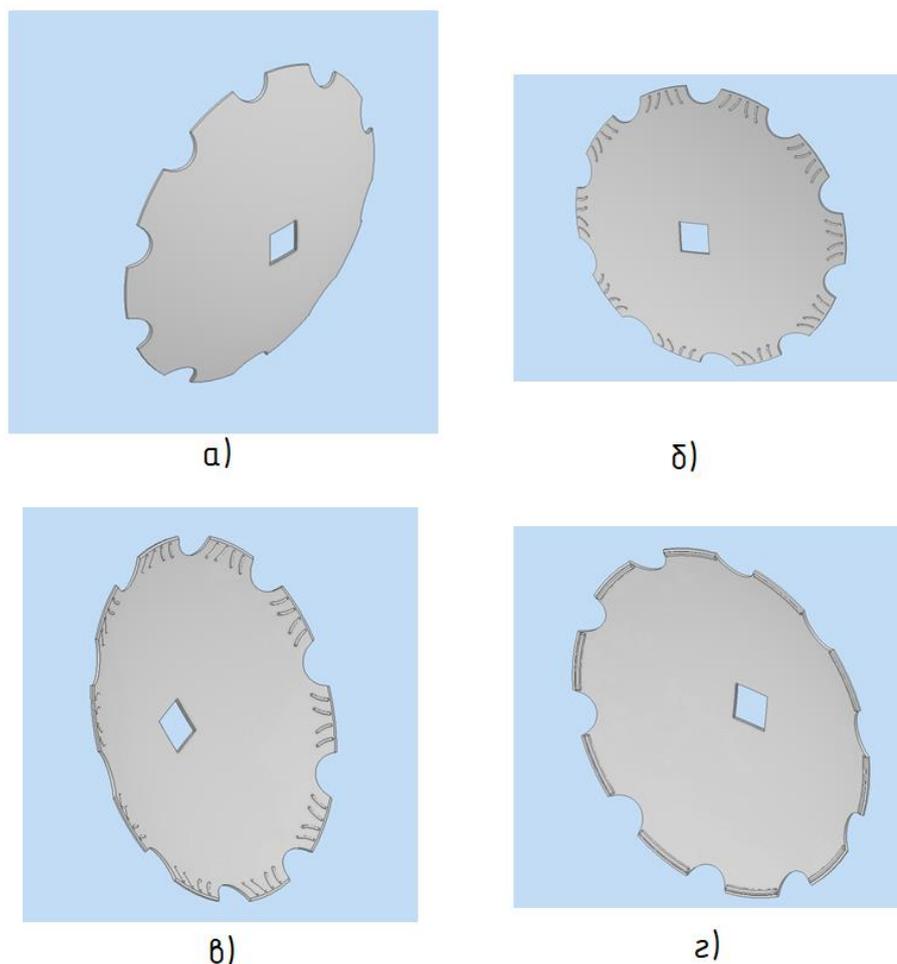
Объёмные 3D модели дисков бороны: а) в заводском исполнении; б) с наплавкой на внешней поверхности зубьев прерывистыми валиками; в) с наплавкой на внутренней поверхности зубьев прерывистыми валиками; б) с наплавкой на внутренней поверхности зубьев двумя перекрывающимися валиками.
